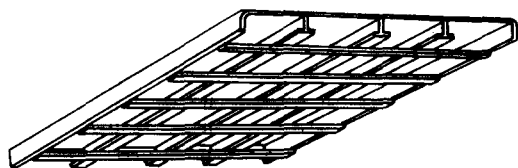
焊接 T 形骨架增强刚度
